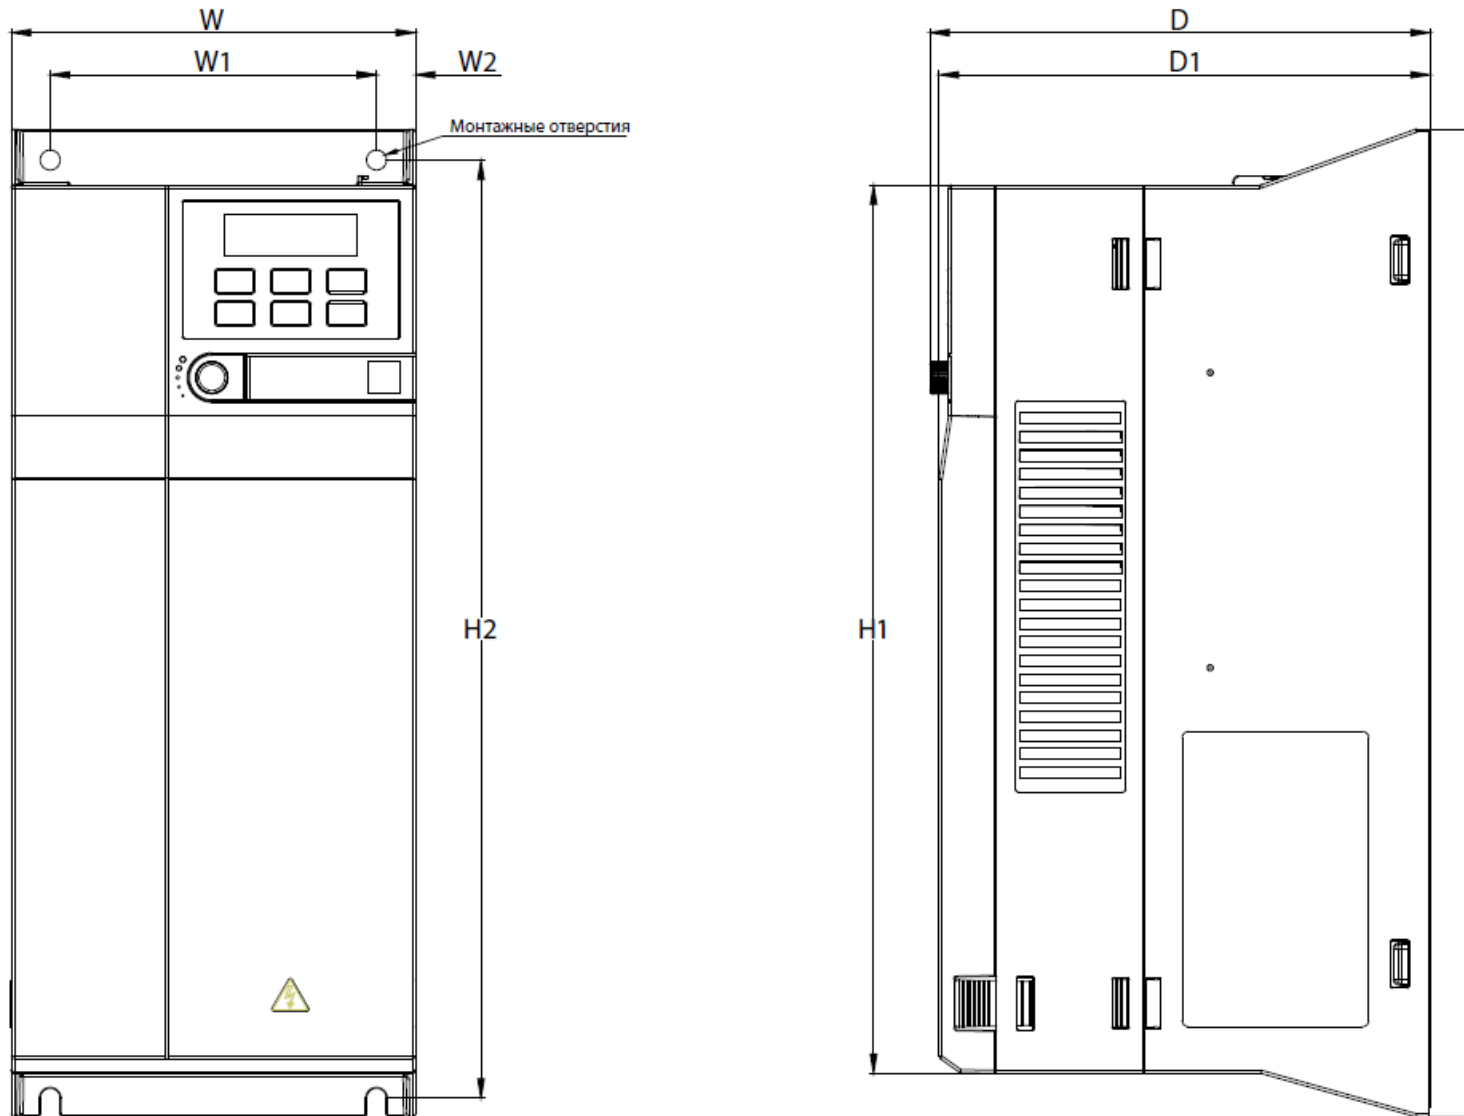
Чертеж преобразователя частоты типоразмер А3
